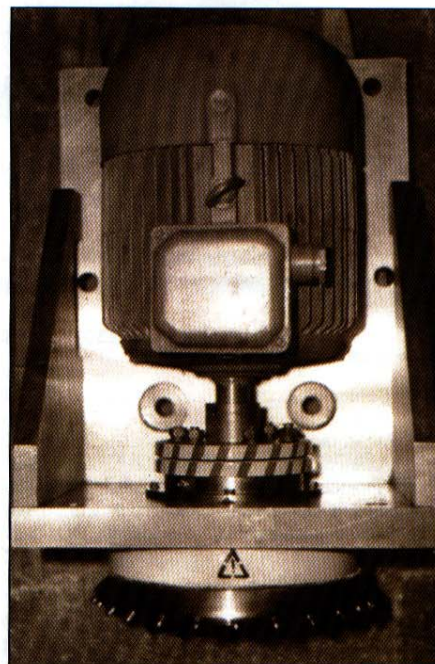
Агрегатная фрезерная головка на подшипниках качения.
